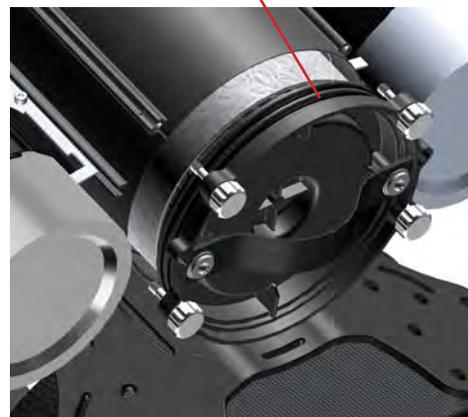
Окончательная установка крышки в корпус картриджа.
